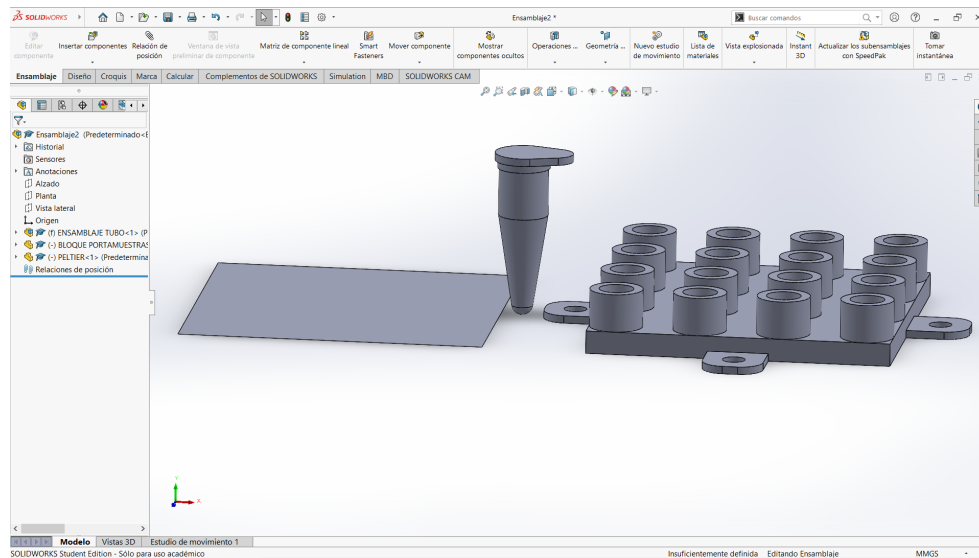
Ensamblaje tubo, celda Peltier y bloque portamuestras para ensamblaje
